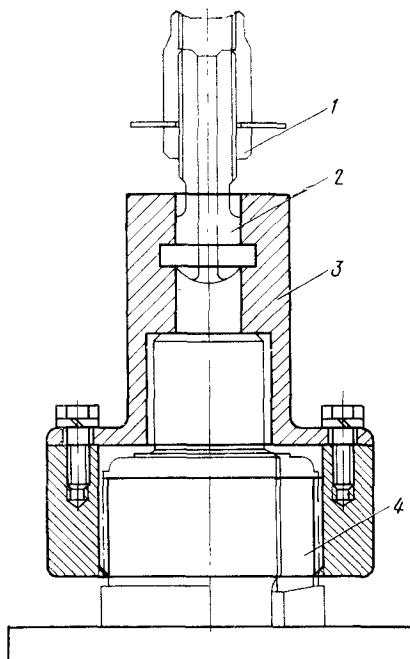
Приспособление для затяжки контргаек штанг механизма газо-распределения:
